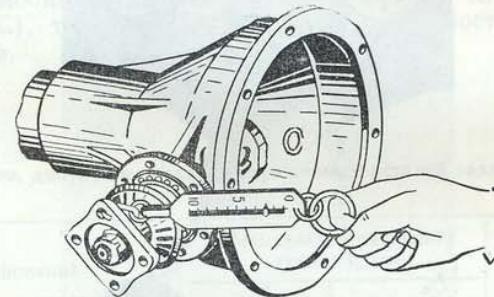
Проверка затяжки подшипников ведущей шестерни
